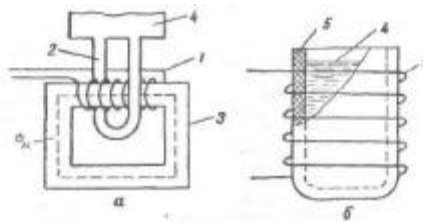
Принципиальные схемы индукционного нагрева: а — схема печи с железным сердечником; б — схема печи без сердечника; 1 — первичная обмотка (индуктор); 2 — кольцо, выполненный металл; 3 — железный сердечник; 4 — металлическая оболочка; 5 — футеровка печи (тигель)
